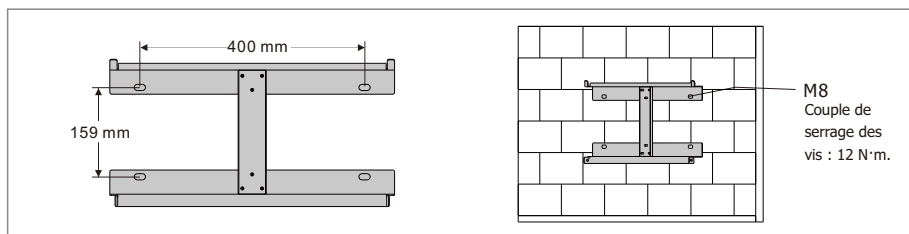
Installation de la plaque de suspension de l'onduleur
